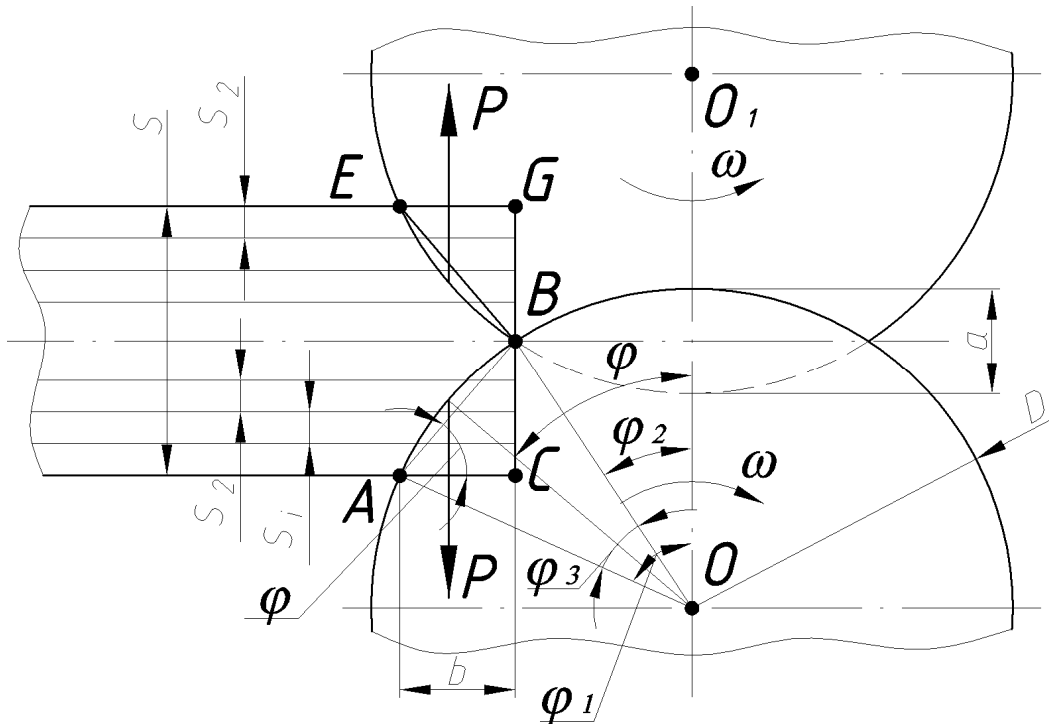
Розрахункова схема для визначення зусилля різання багат шарової гладкої конвеєрної стрічки дисковими ножами
